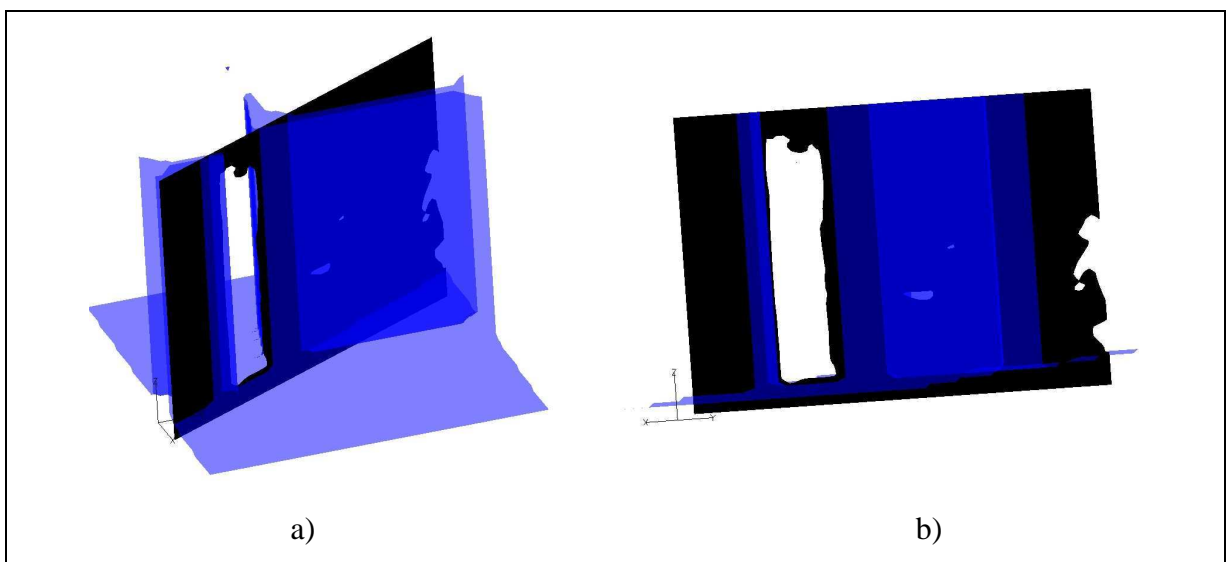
a) Vista em perspectiva do plano passando pela ranhura b) Vista em planta.
